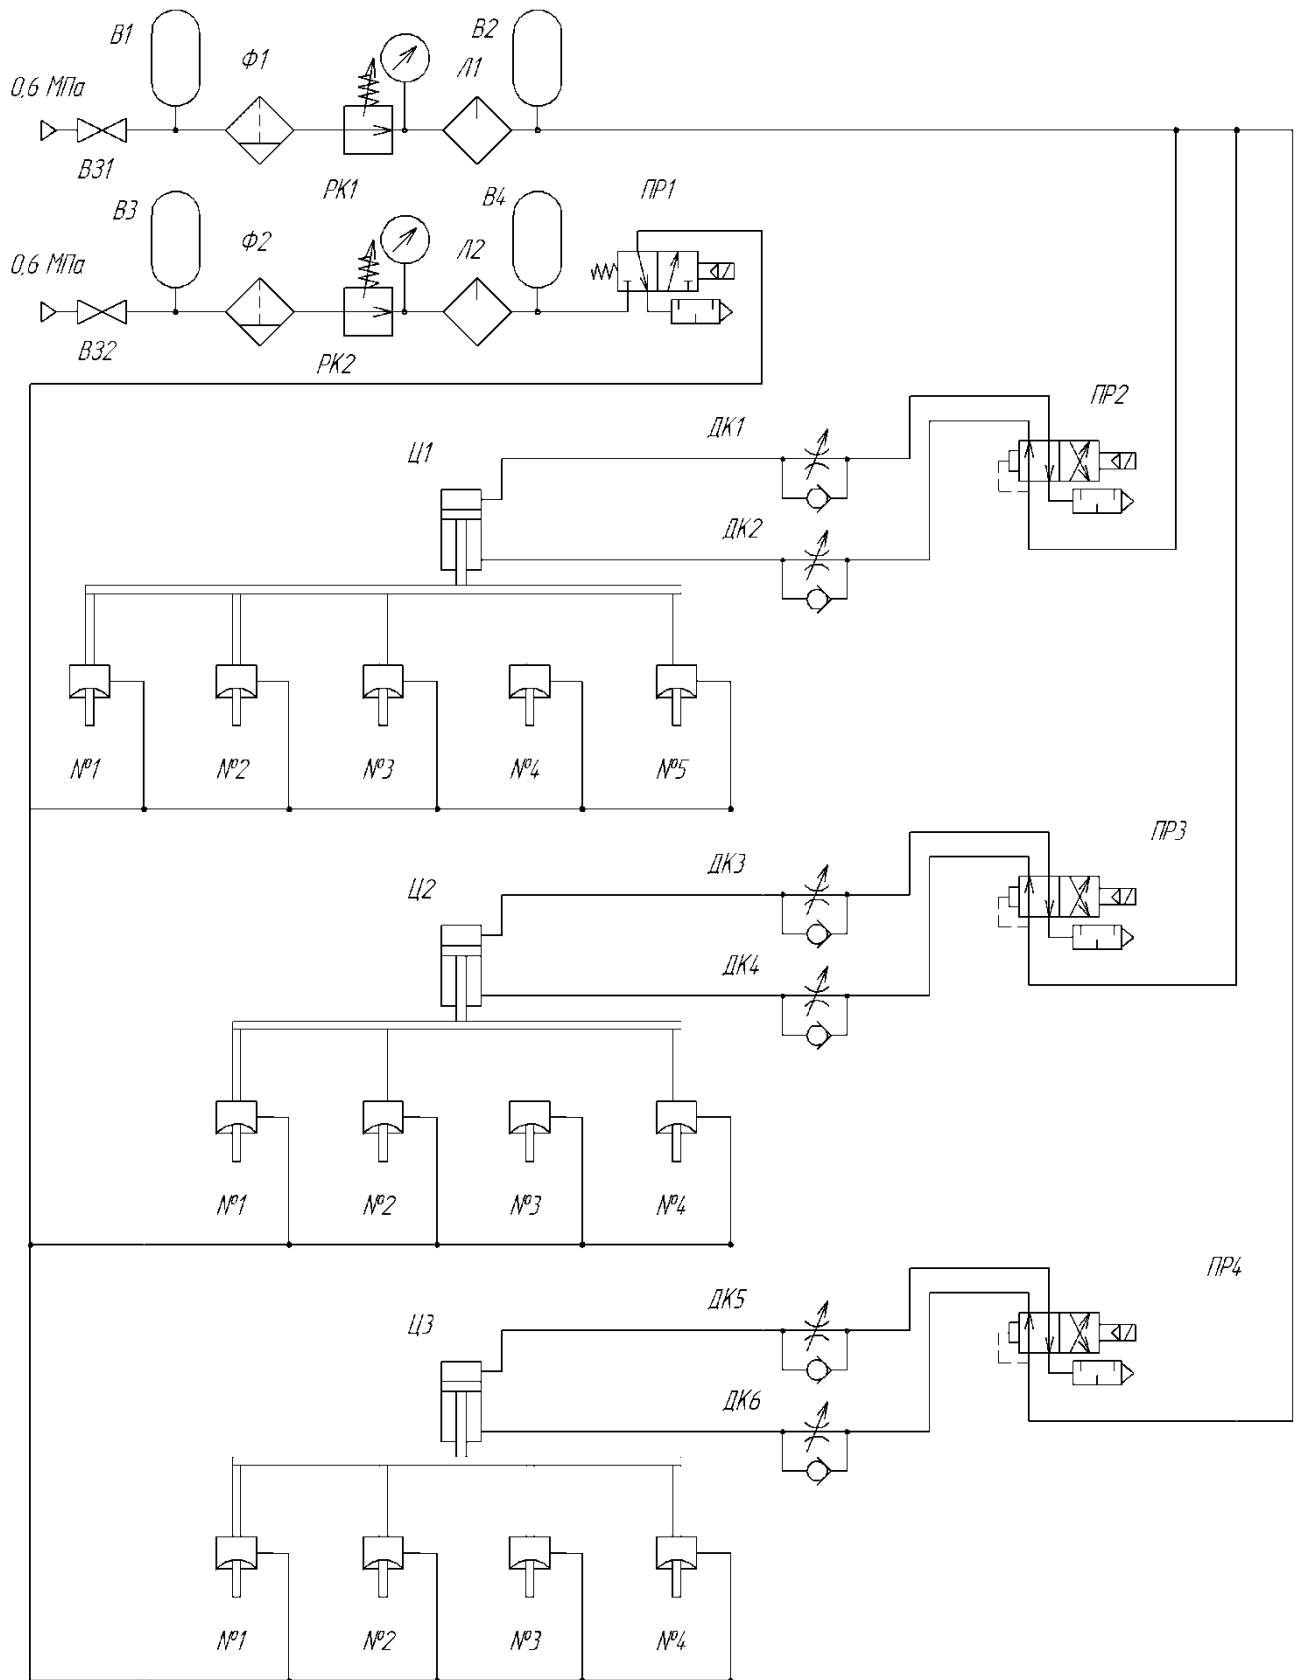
Пневматическая схема участка сварки №1
